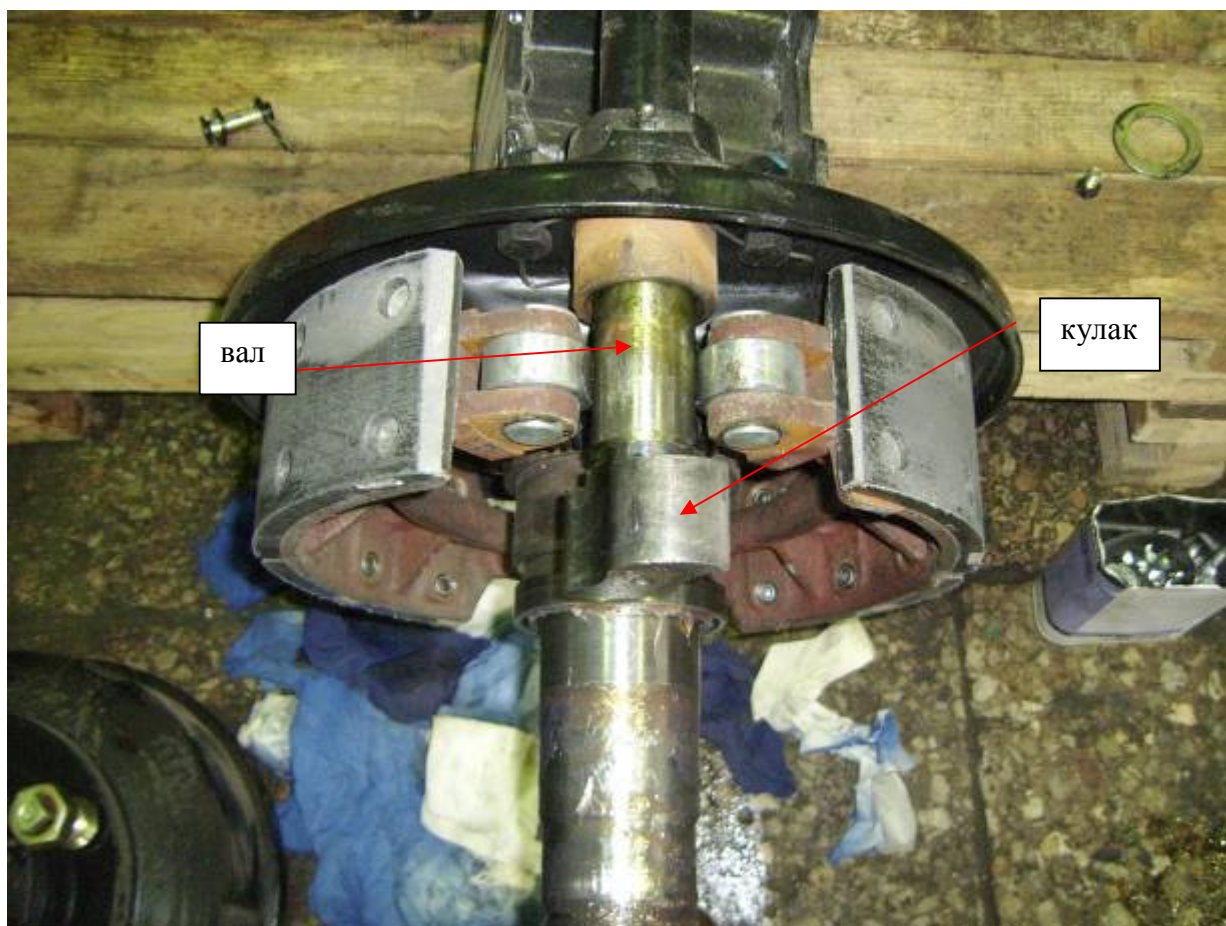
Положение разжимного кулака перед установкой механизма (вид сверху)
